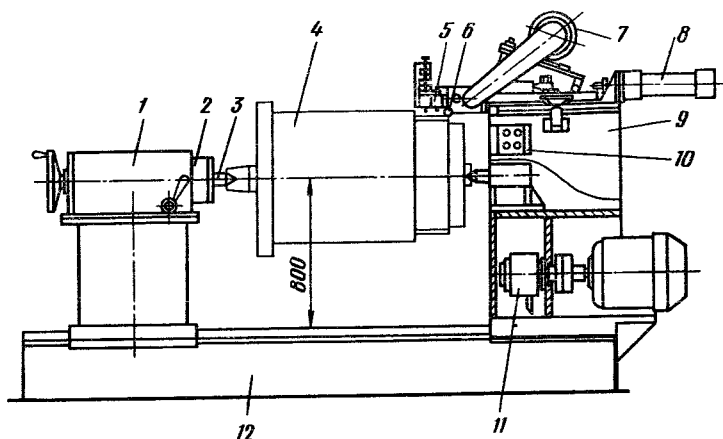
Станок-полуавтомат для продороживания коллекторов
